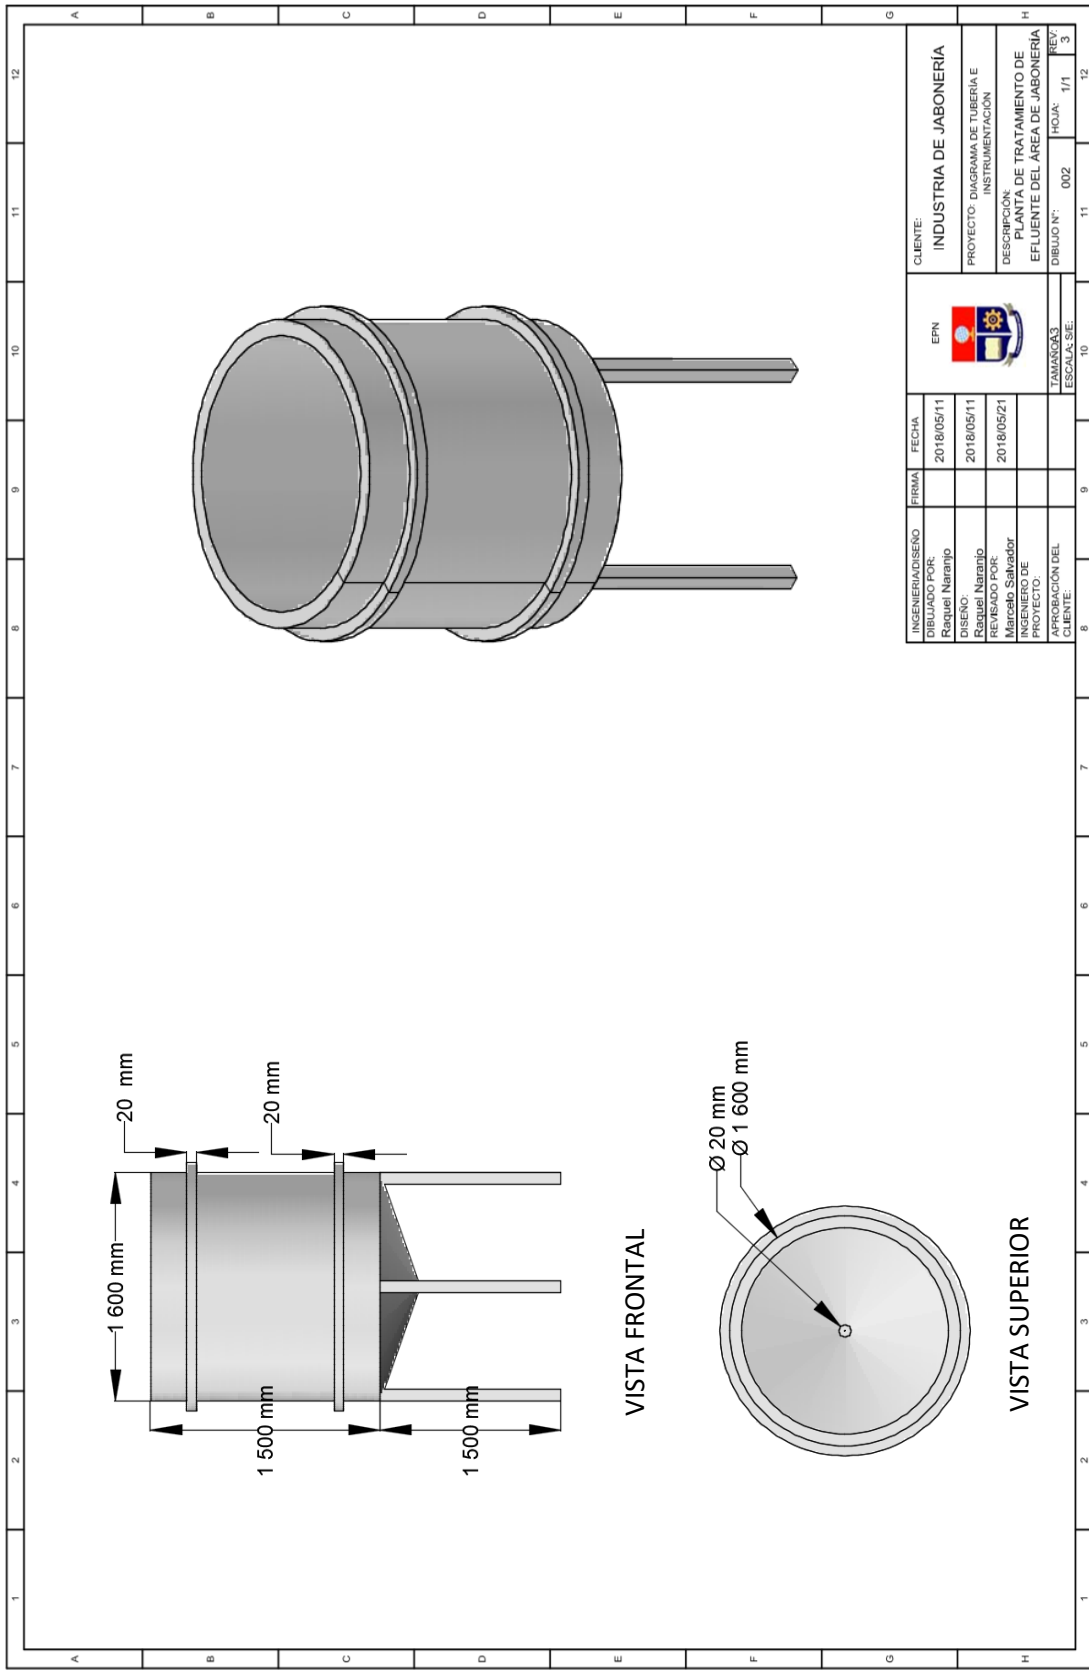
Planos de elevación del tanque del sedimentador primario
